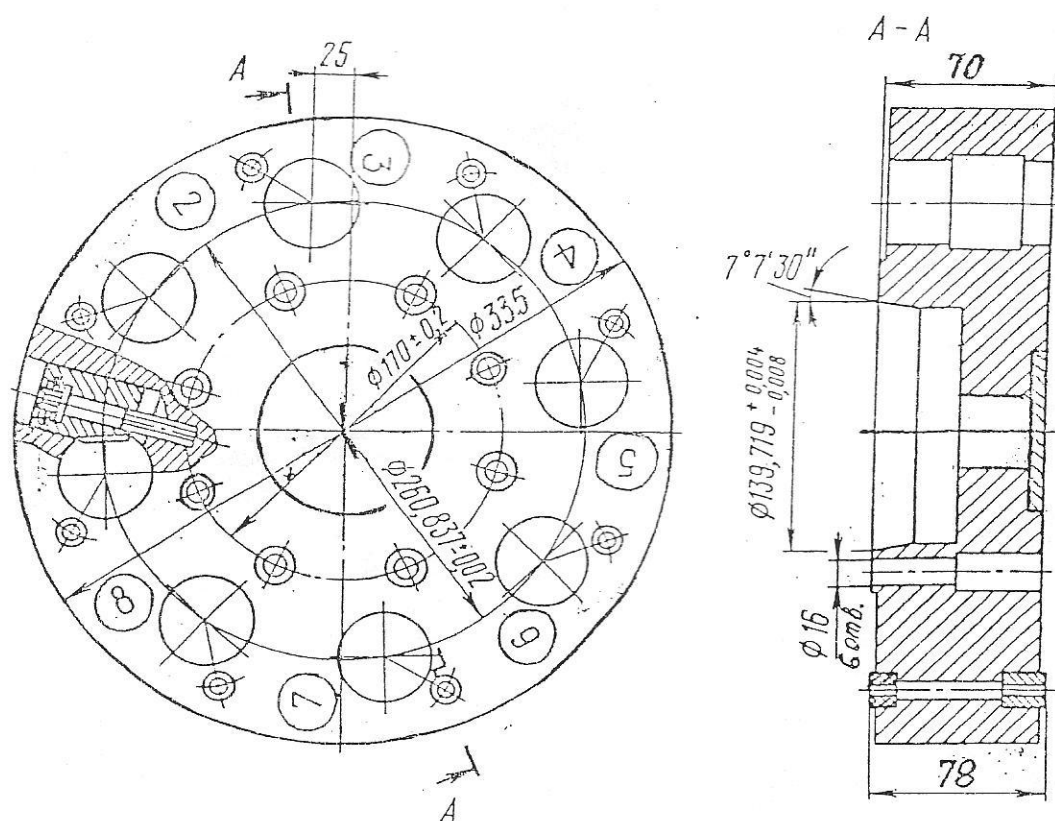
Инструментальный диск шестипозиционный УГ9326.0300.000
